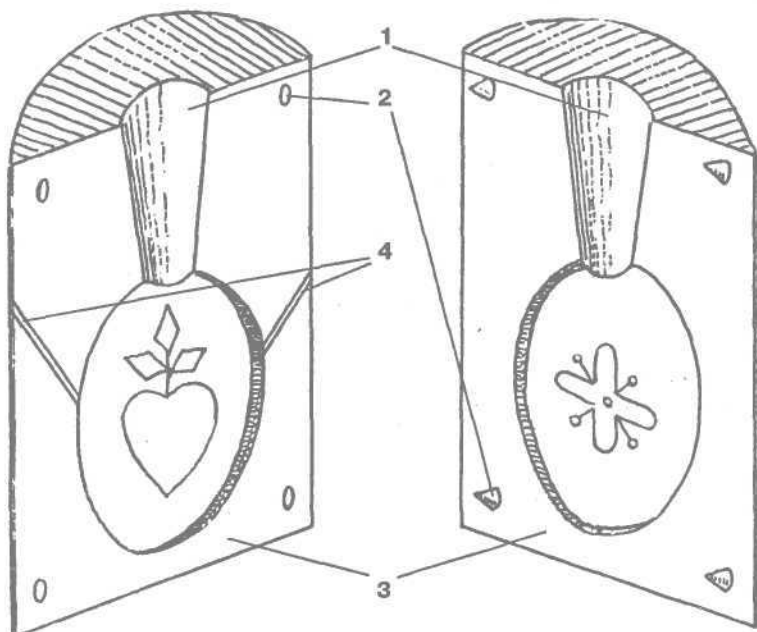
Литейная форма из глины: 1 — литник; 2 — фиксаторы; 3 — форма; 4 — выпоры
